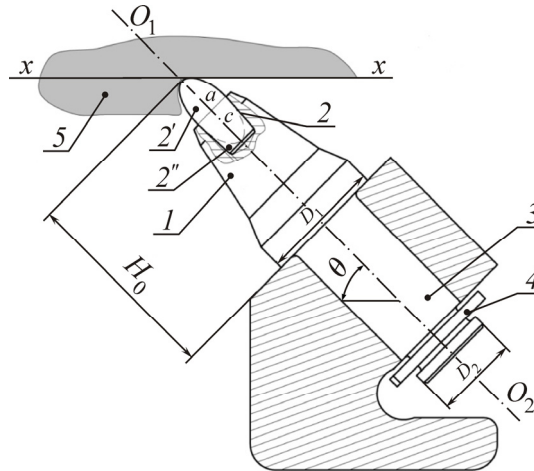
Тангенциальный поворотный резец с твердосплавной вставкой, режущая часть которой выполнена в форме эллипсоида вращения: 1 — головная часть резца; 2 — армирующая твердосплавная вставка; 2' — рабочая ступень вставки, 2'' — посадочная ступень вставки; 3 — опорно-поворотная часть резца; 4 — хвостовик с замком для удержания резца в опорном кулаке; 5 — разрушаемая среда
